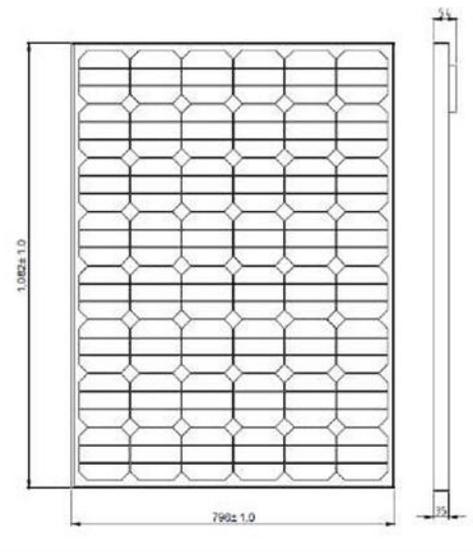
Hoja técnica de panel C-120. Fuente, www.proenergy.com.mx/productos.php
